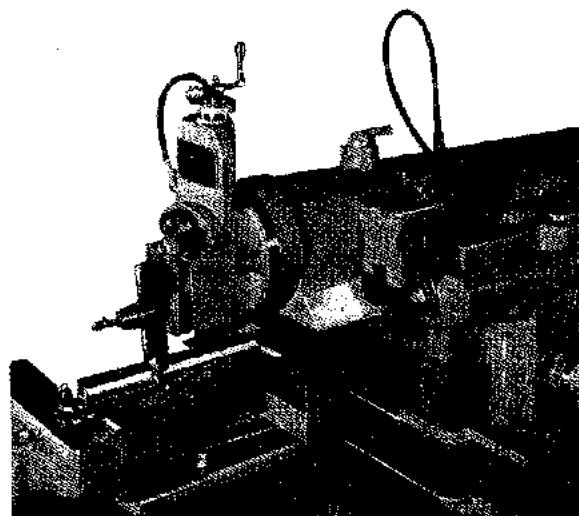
Dispositivo de avance mecánico del cabezal de herramienta montado en una limadora hidráulica (Rockford Machine Co.)
